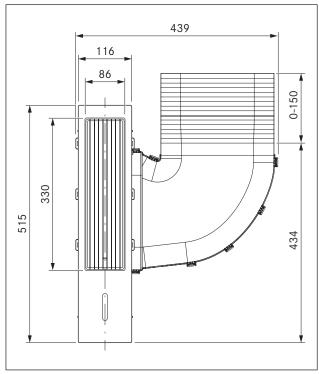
CKA2/CKA2AB Gerätemaße Draufsicht
